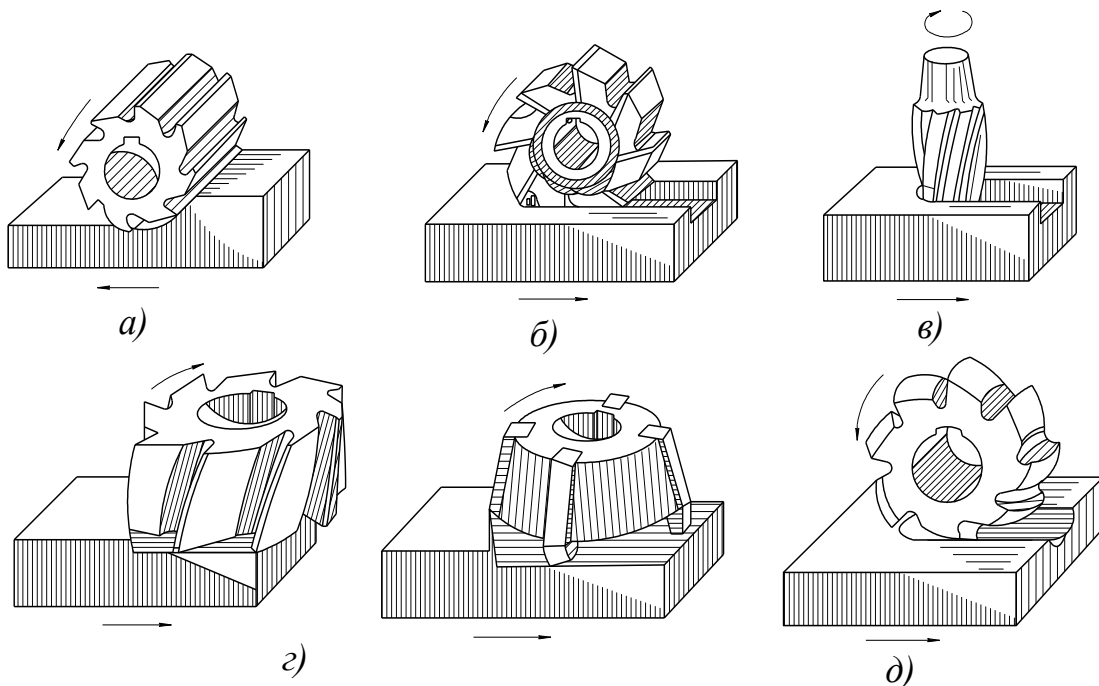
Основні типи фрез: *a* – циліндрична; *б* – дискова; *в* – кінцева; *г* – торцева; *д* – фасонна
